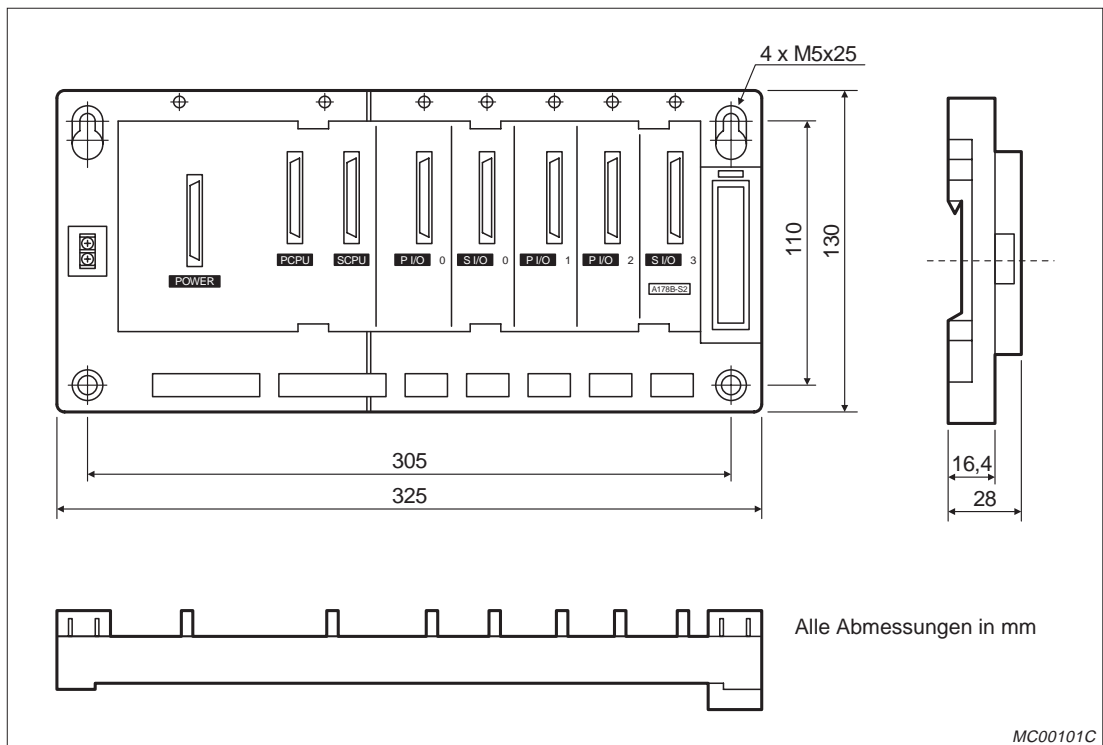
Abmessungen des Hauptbaugruppenträgers A175B
